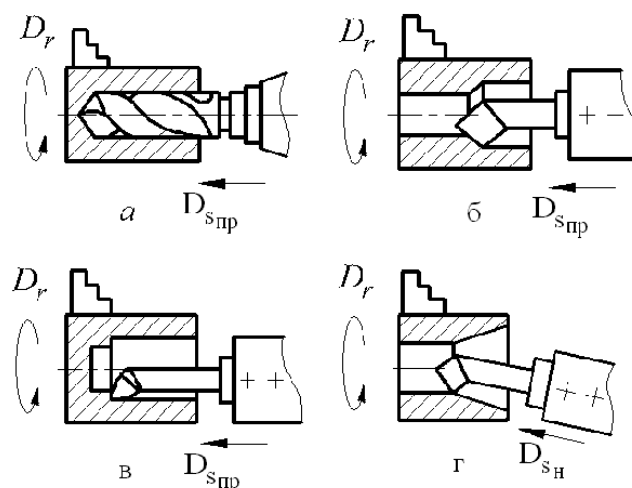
Типовые схемы обработки цилиндрических и конических отверстий в заготовках на станках токарной группы
